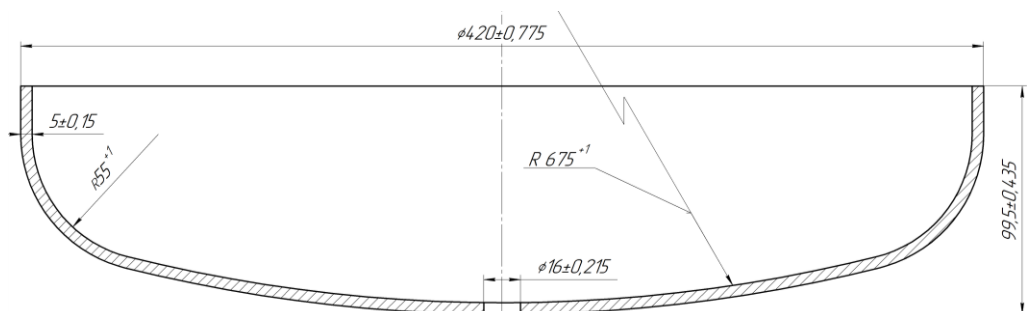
Деталь «днище» ресивера фільтрувальної установки для дробильноструменевих і дробометних камер
